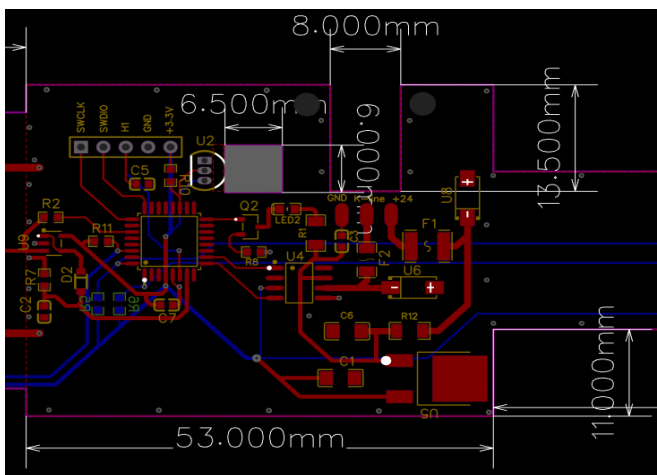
Креслення другої частини друкованої плати модулю вимірювання
